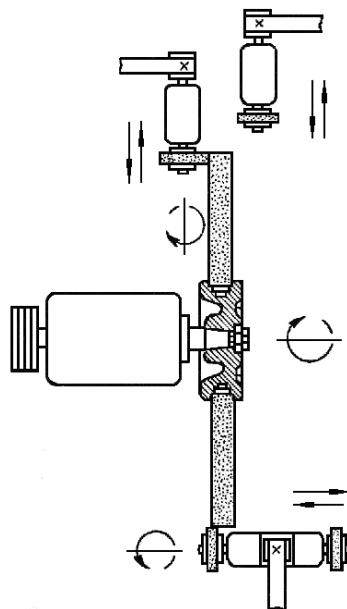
Схема правки торцов и периферии абразивного диска приспособлением с самостоятельным приводом правящего инструмента
